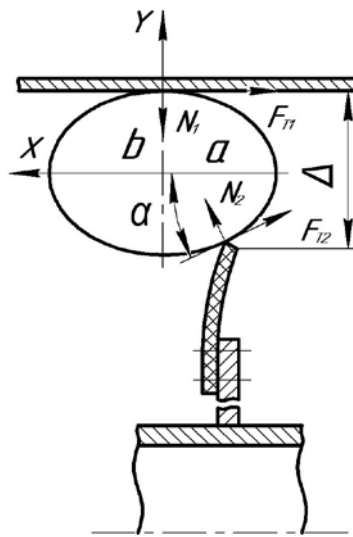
Схема сил, які виникають при попаданні зернини у зазор Δ між еластичною секцією та внутрішньою поверхнею циліндричного кожуха
